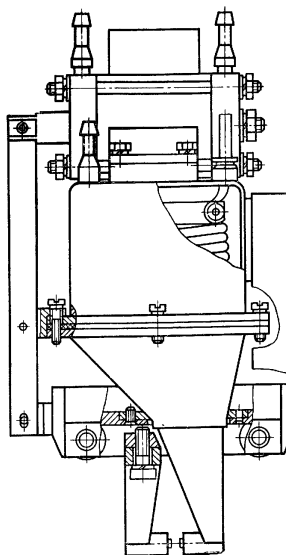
Сварочная головка клещей КТВ-1,5
